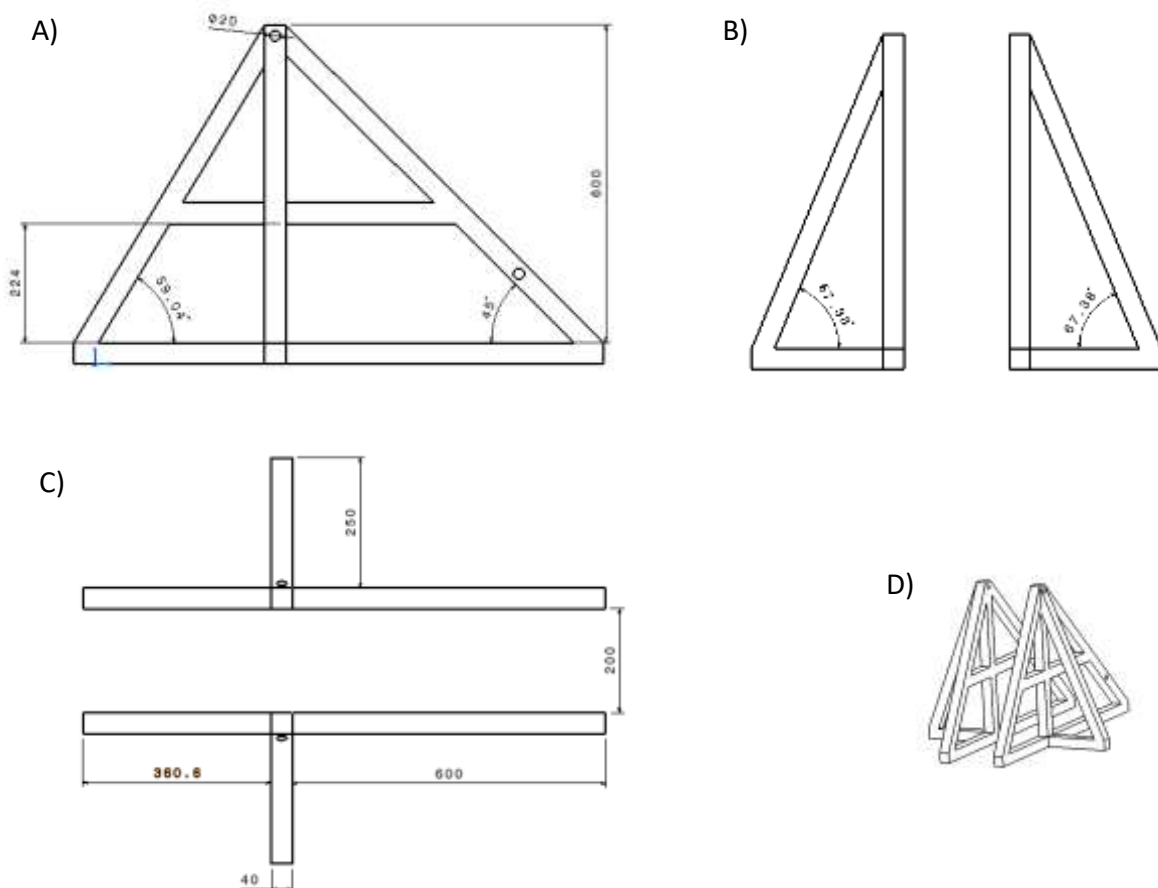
Estructura base. A) Vista frontal. B) Vista lateral izquierda. C) Vista de planta. D) Vista isométrica.
